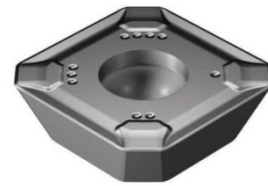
Конструкция торцевой фрезы фирмы «Sandvik Coromant» CoroMill R245-063Q22-12M:
